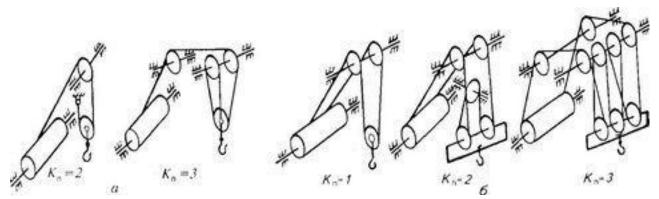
Схемы механизмов подъема крюковой подвески
